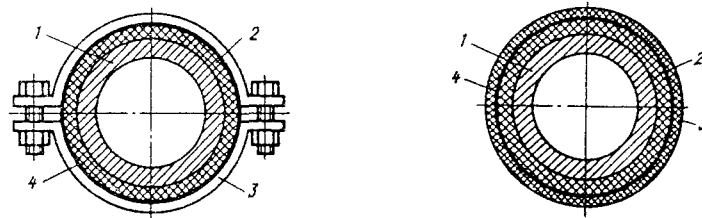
Опрессовка изоляции втулки контактных колец хомутами:
